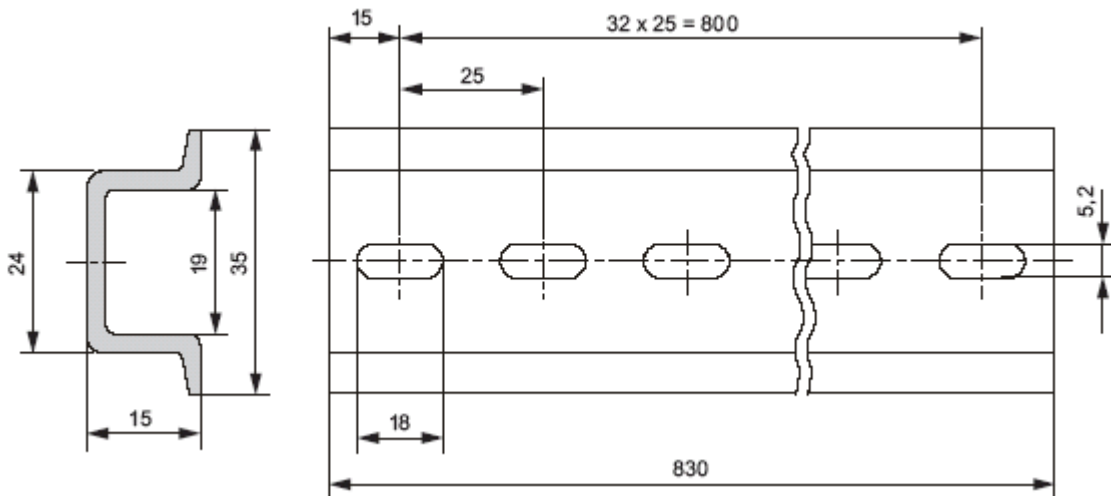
Габаритный чертеж 830-миллиметровой стандартной профильной шины
